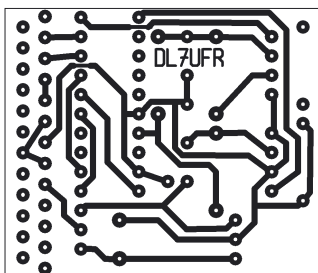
Layout des Wandler für die RS232-Schnittstelle
